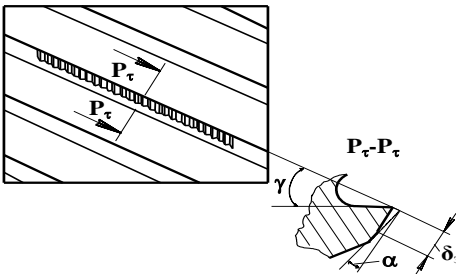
Схема зношування осьової циліндричної фрези
